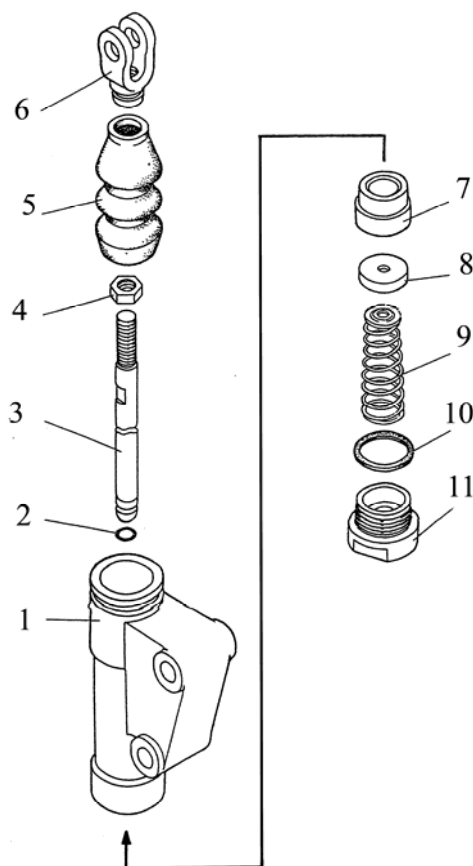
Главный цилиндр управления сцеплением на реверсе.
